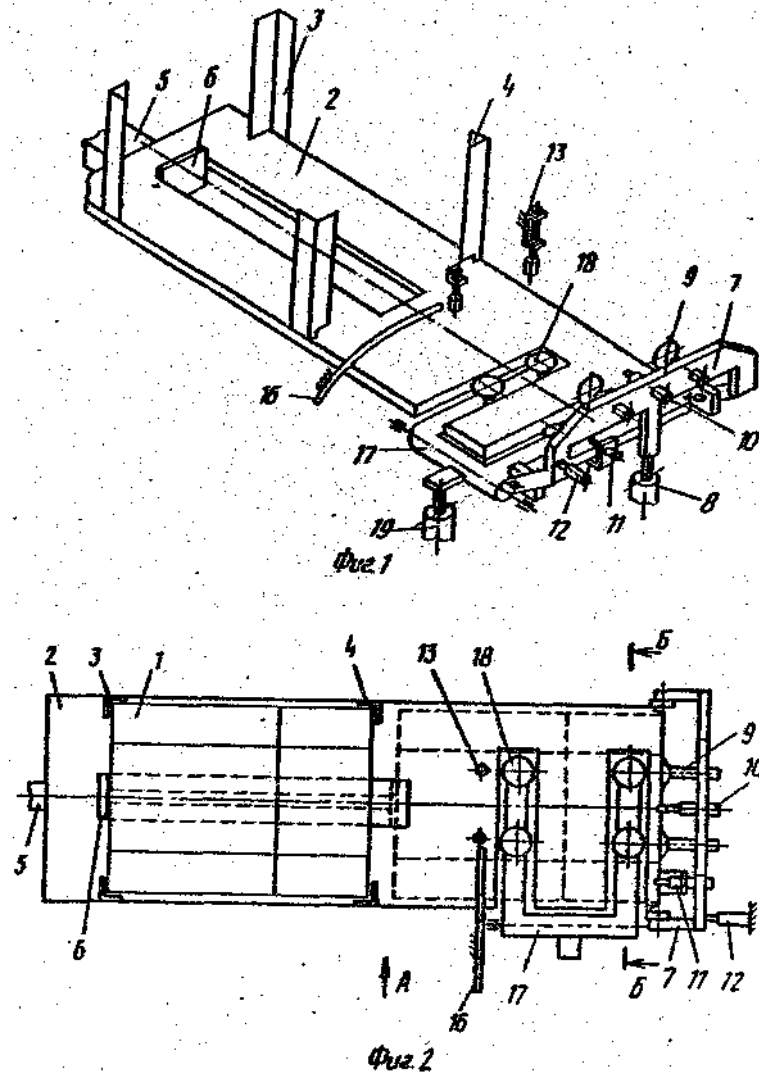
Загальний вигляд пристрою для формування коробів із плоско складених картонних заготовок
